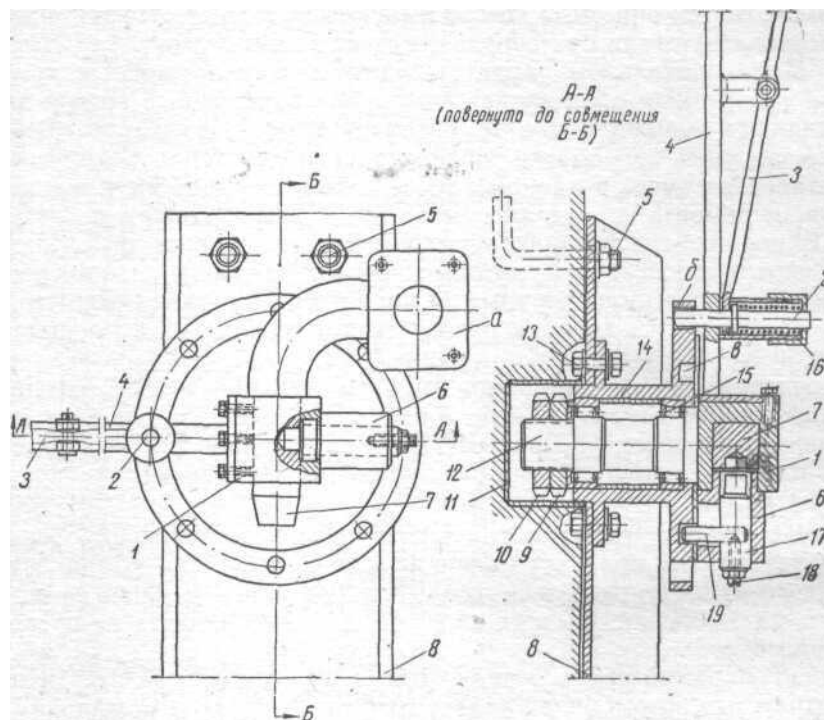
Стационарный стенд для разборки и сборки двигателя
